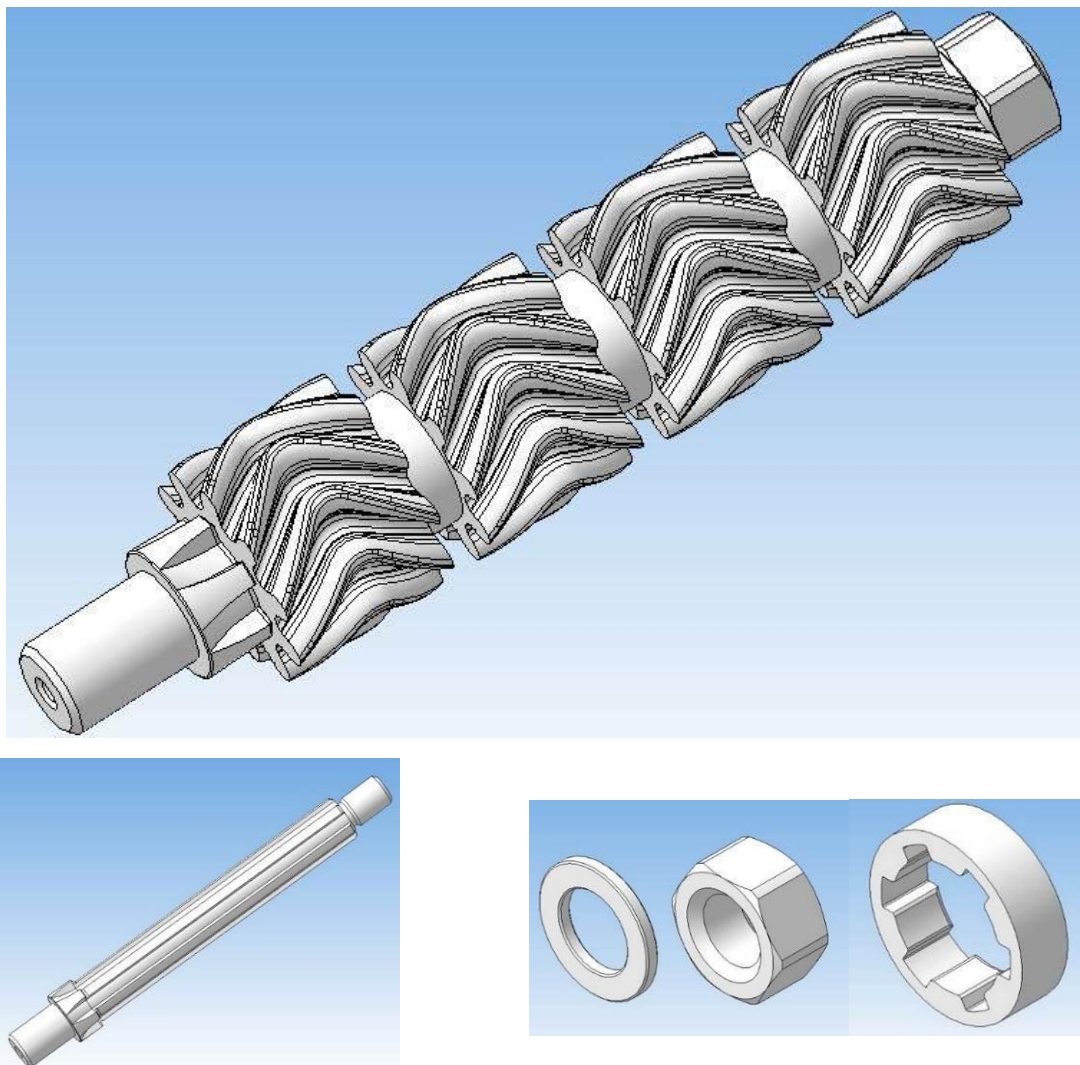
Комп'ютерна модель оправки для виготовлення зубчастих коліс та її деталей
